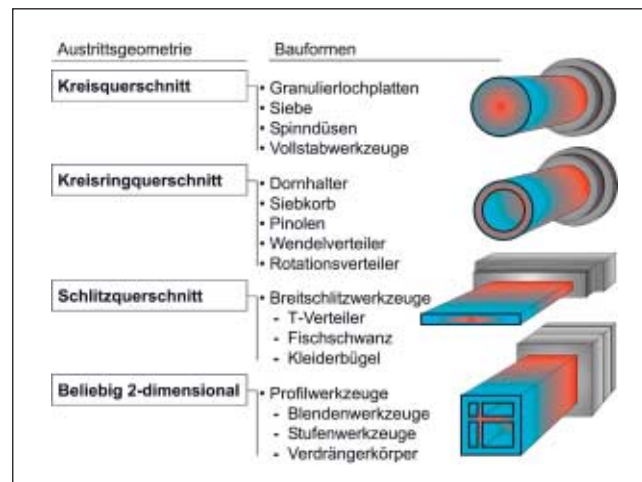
Übersicht der Bauformen von Extrusionswerkzeugen
